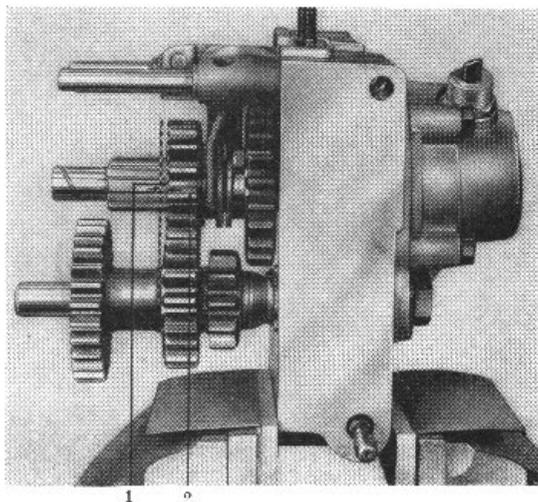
Schaltrad für 2. und 3. Gang zum Vorgelegerad ausfluchten
